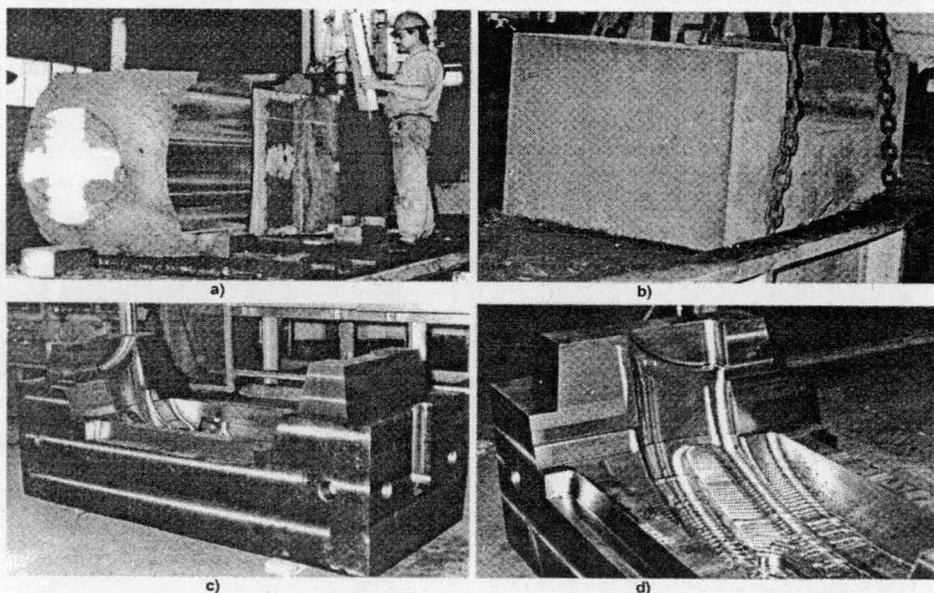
Exemplo de molde produzido com aço VP20 ISO. a) bloco pré-esboçado durante sua fabricação e b) após tratamento térmico, pesando 14.800 kg; c) e d) molde após usinagem de desbaste realizada pelo fabricante, agora pesando 8.400 kg.
